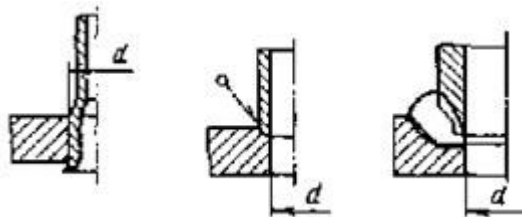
Типи з'єднання труб (штуцерів) з розрахунковою деталлю.
